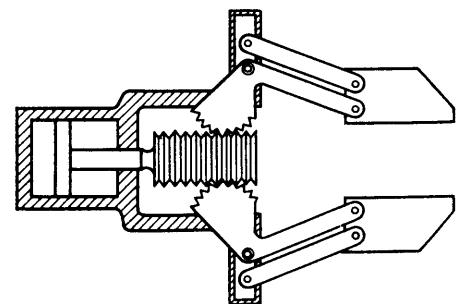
Захват с параллельными захватываемыми поверхностями и механизмом реечной передачи
